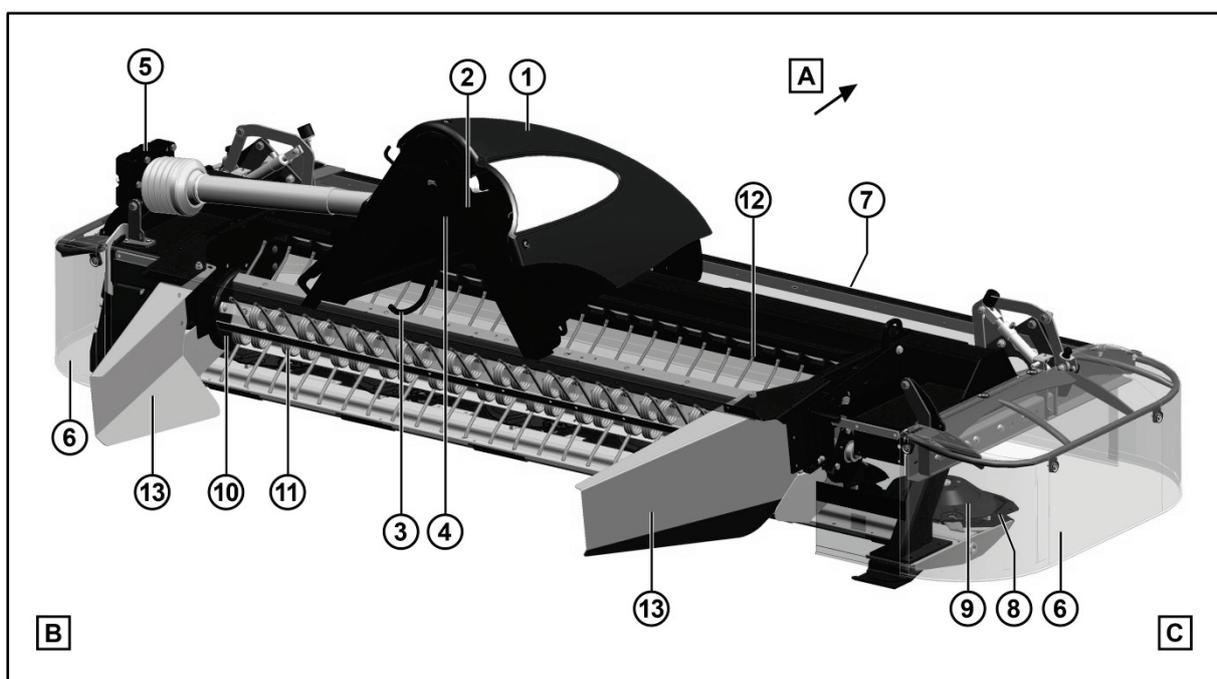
Componentes de la máquina SM 3060 FP-KC
